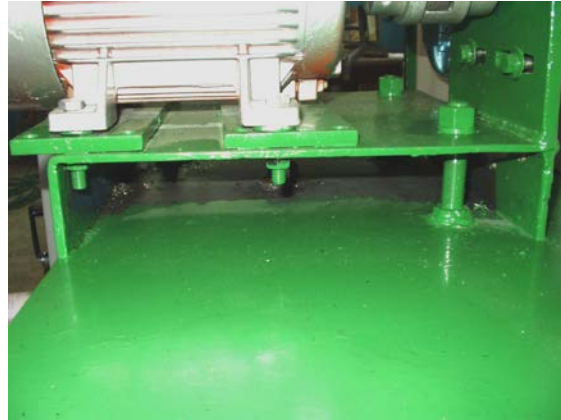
Sujeción de la base del motor y bomba. Fuente: Propia.
